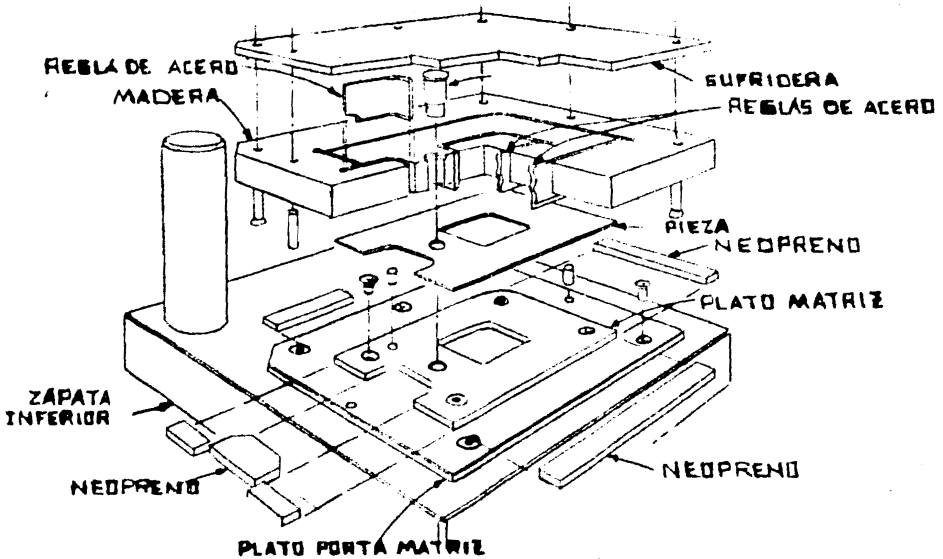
Troquel Compuesto de Reglas de acero de corte y Punzonado.
